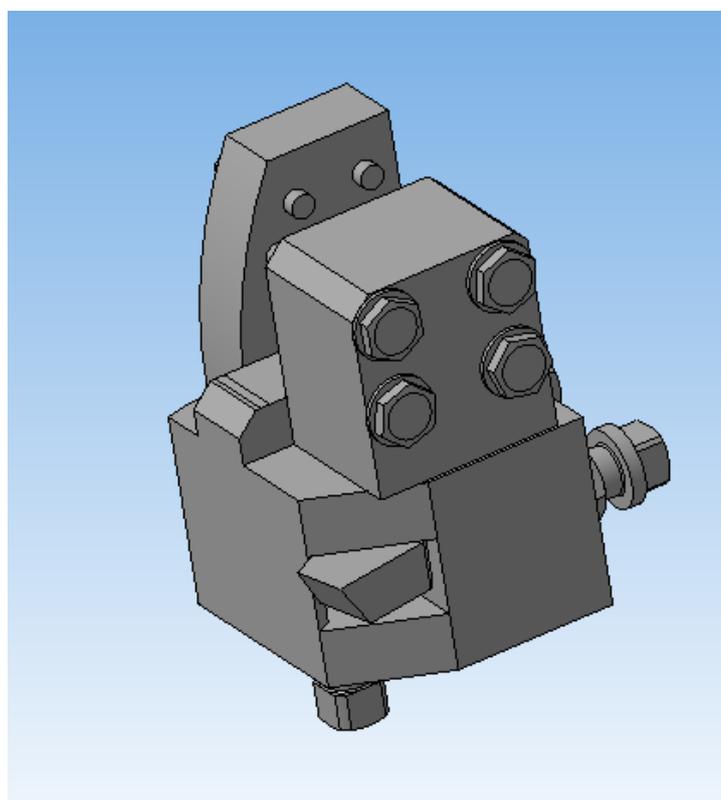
Твердотельная модель крепежной части фрезы
